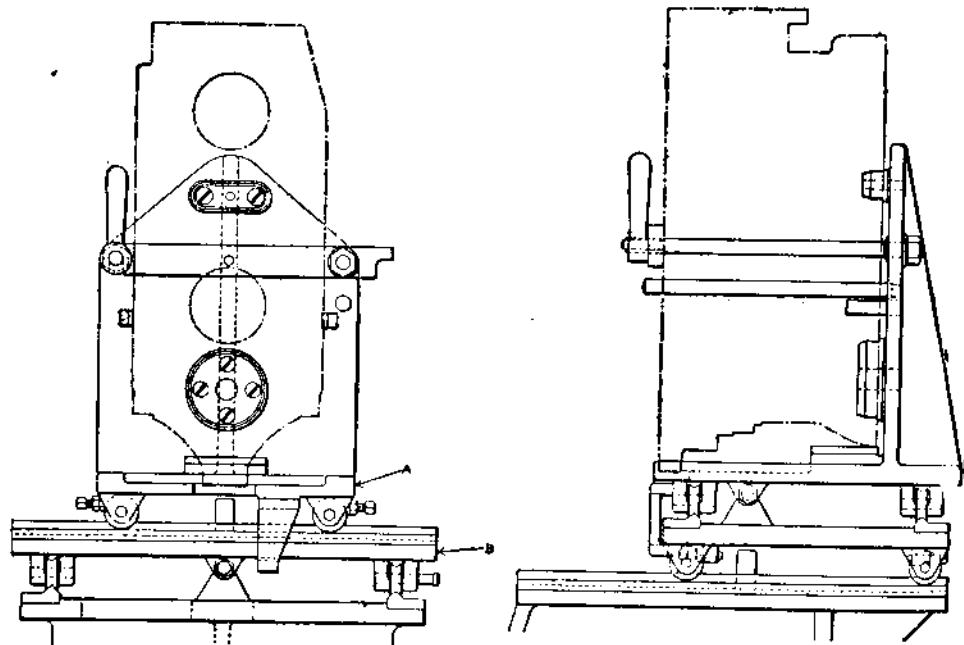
Приспособление Форда для закрепления блока при нарезке.
